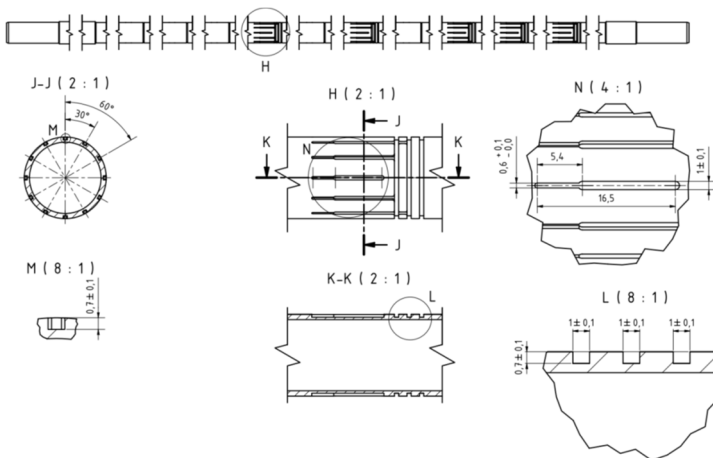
Technische Zeichnung des Messrohres aus Alloy 201 mit Nutbild und Positionierung der Thermoelemente für Messebenen mit 12 Thermoelementen.
